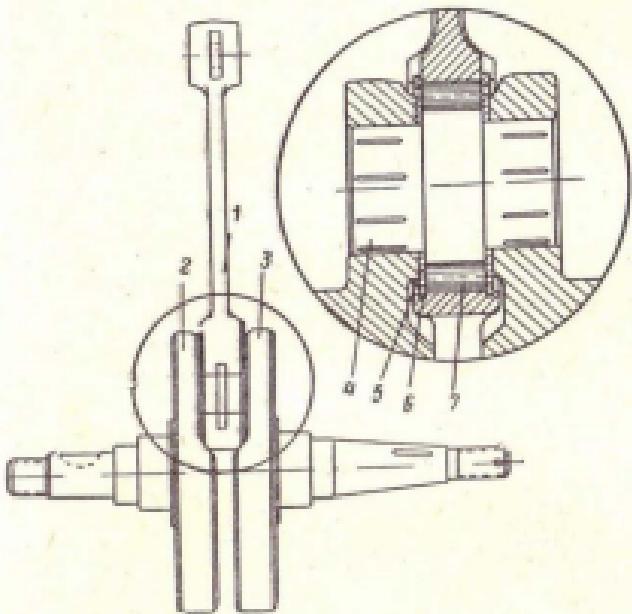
Сборка коленчатого вала двигателя мотороллера „Бэтка“.
